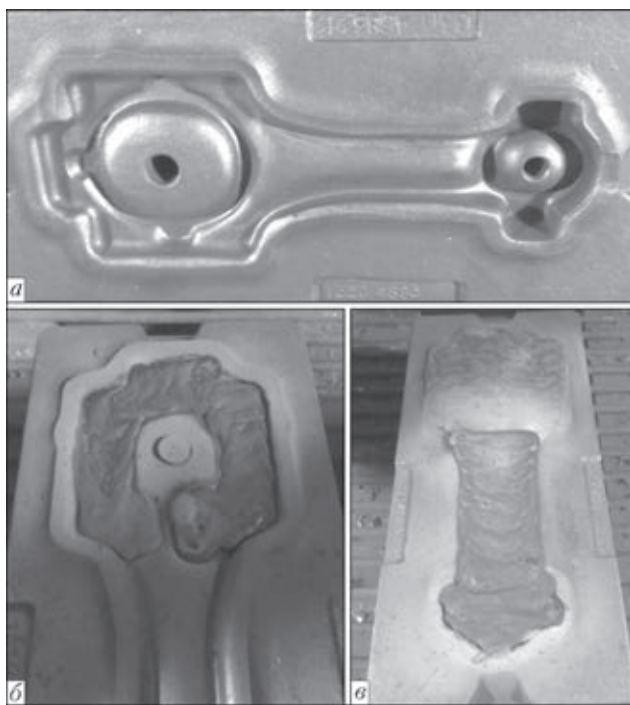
Ремонт штампа детали (шатуна): а — состояние изношенной рабочей поверхности штампа; б — наплавка валика-ми без колебаний; в — наплавка с колебаниями
